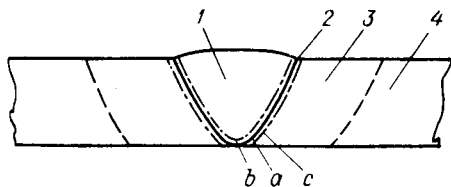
Схема поперечного разреза сварного соединения
